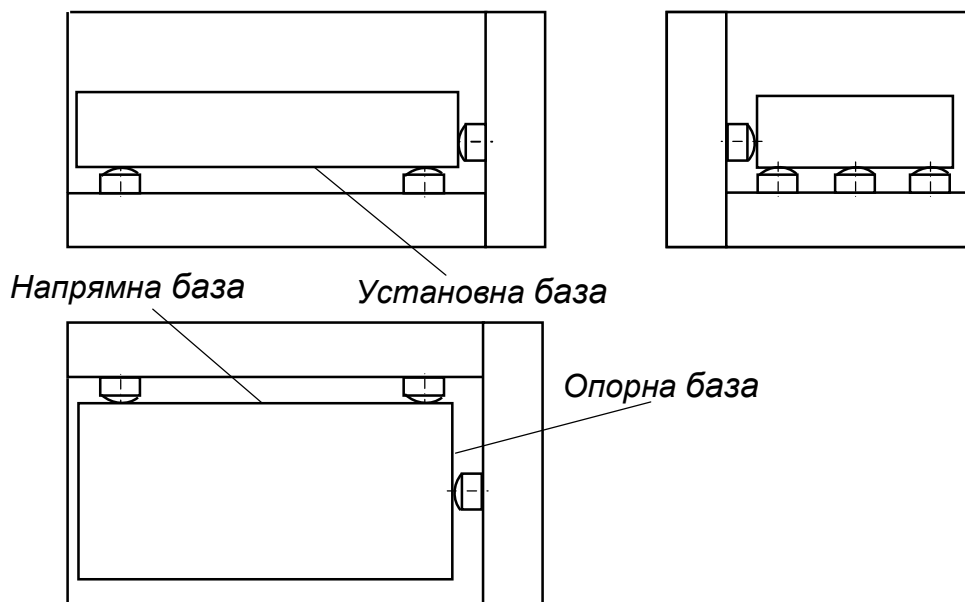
Приклад використання установної, напрямної та опорної баз для установалення призматичної заготовки у верстатному пристрої
